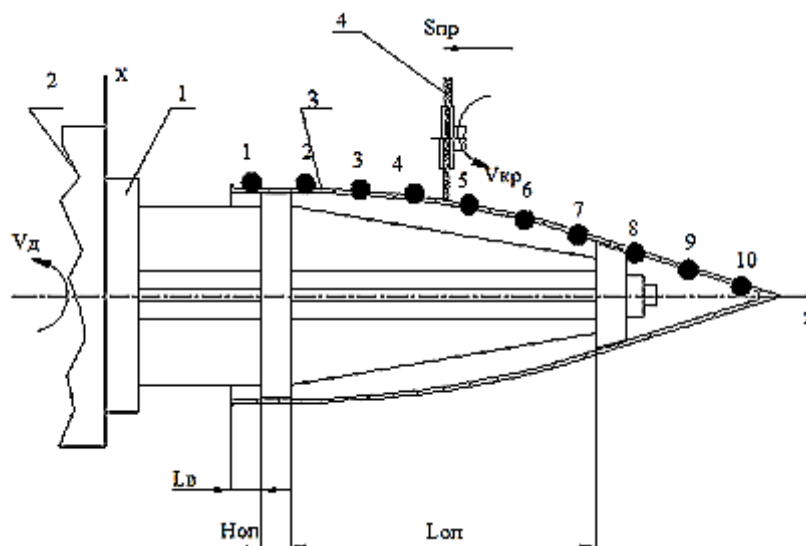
Схема установки заготовки на операции наружного шлифования изделия:
